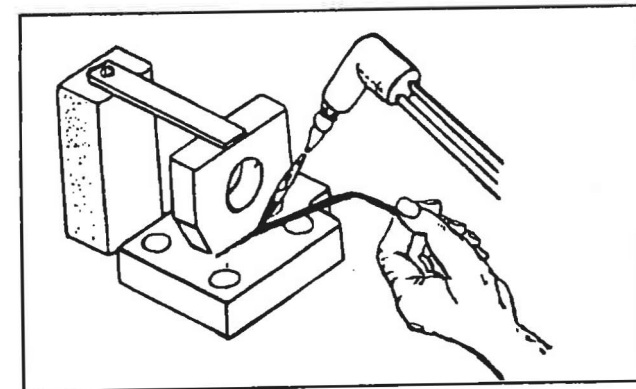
SOLDEO FUERTE O BLANDO CON SOPLETE
